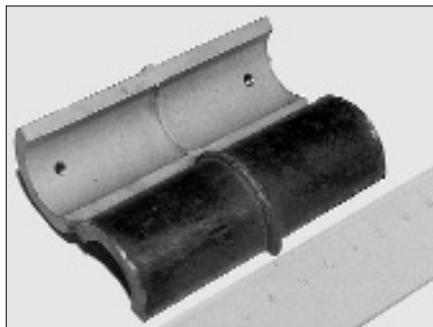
Внешний вид образцов труб диаметром 32×4 мм после сварки
